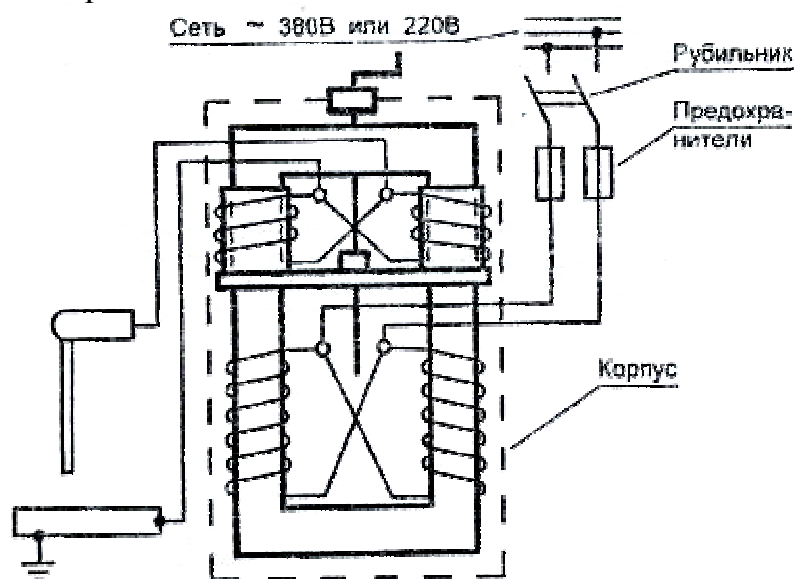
Принципиальная электрическая схема сварочного трансформатора с подвижными катушками вторичной обмотки
